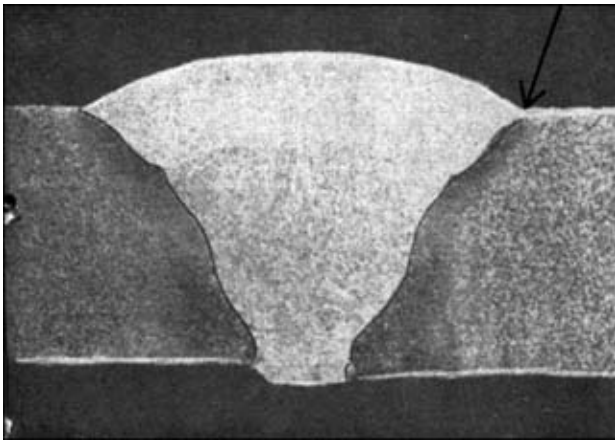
Макрошлиф кольцевого сварного соединения, полученного ручной электродуговой сваркой: стрелкой показано место расположения концентратора напряжений, совпадающее с ЗС
